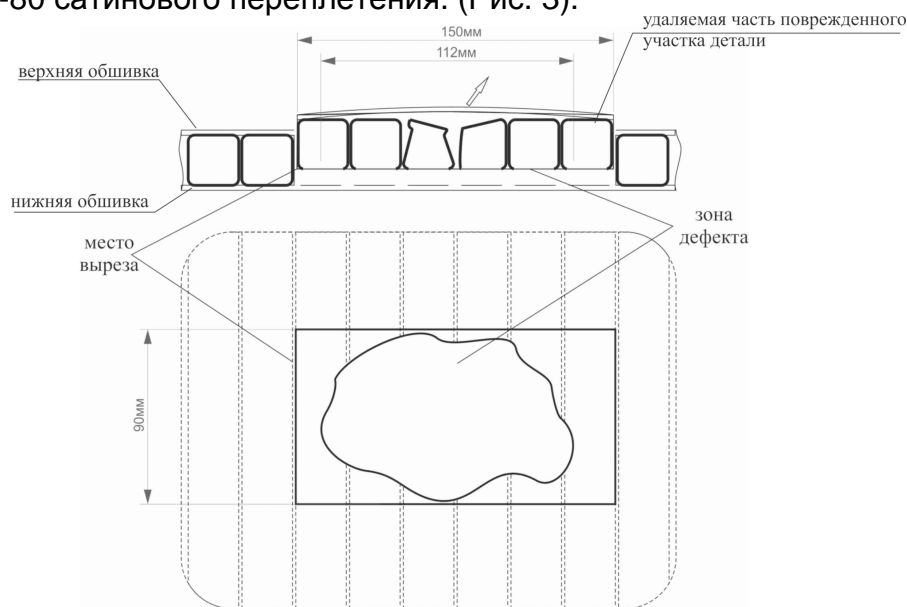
Схема разметки места повреждения трубчатого (сотового) наполнителя с обшивкой, для последующего ремонта
